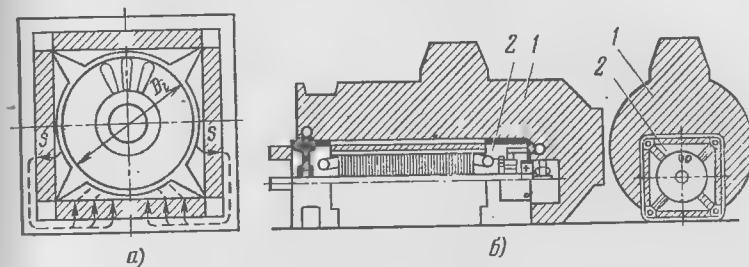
Высокомоментный двигатель с ферритовыми магнитами.
